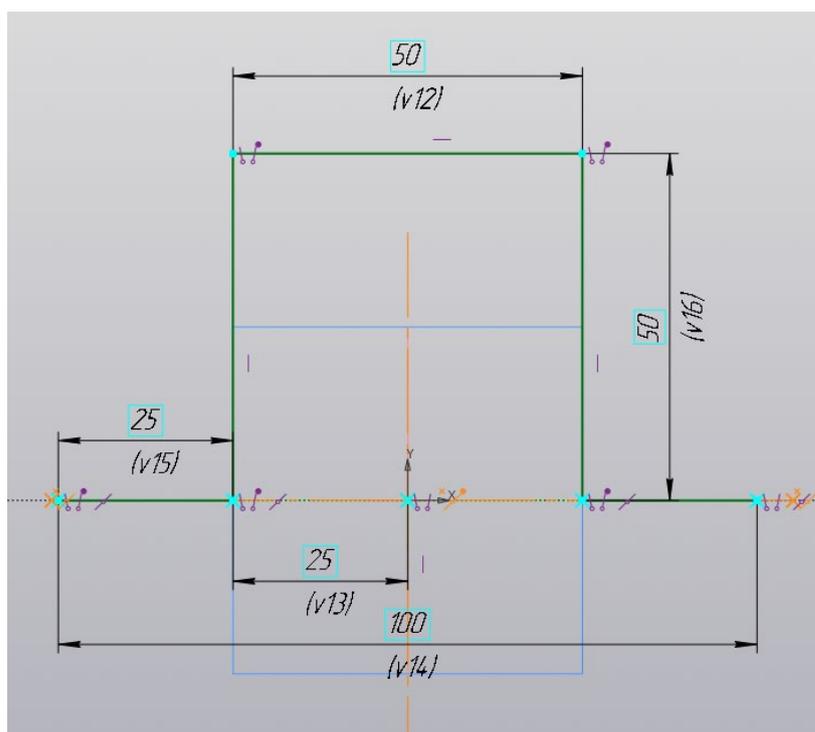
Первый эскиз с геометрическими размерами профиля
